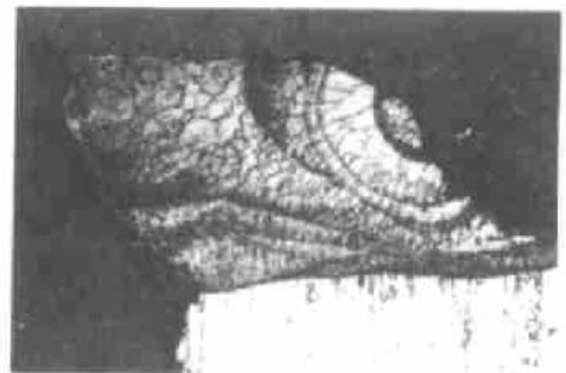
8090Al-Li 合金 YAG 激光焊延迟裂纹(160×)
